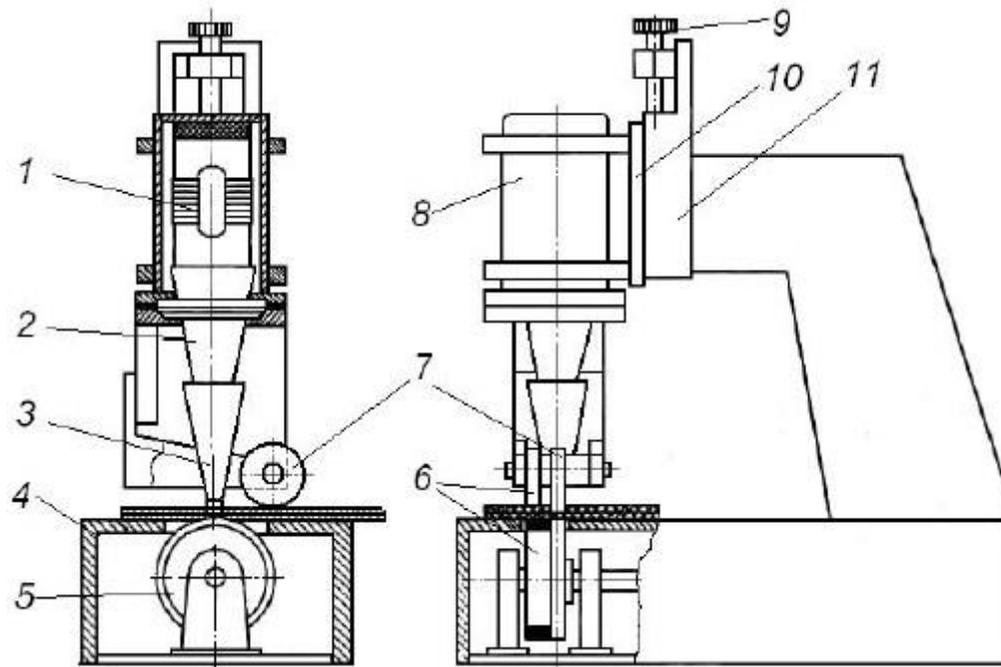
Устройство сварочной машины модели УПШ-12: 1 – преобразователь; 2 – трансформатор упругих колебаний; 3 – волновод-инструмент; 4 – рабочий стол; 5 – роликовая опора; 6 – протягивающие ролики; 7 – прокатывающий ролик; 8 – сварочный узел; 9 – установочный винт; 10 – подвижная суппорт; 11 – станина
